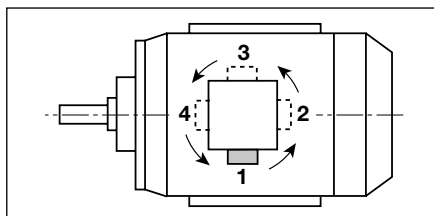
U - Verlaufs der Kabeleinführung auf dem Grundriss
